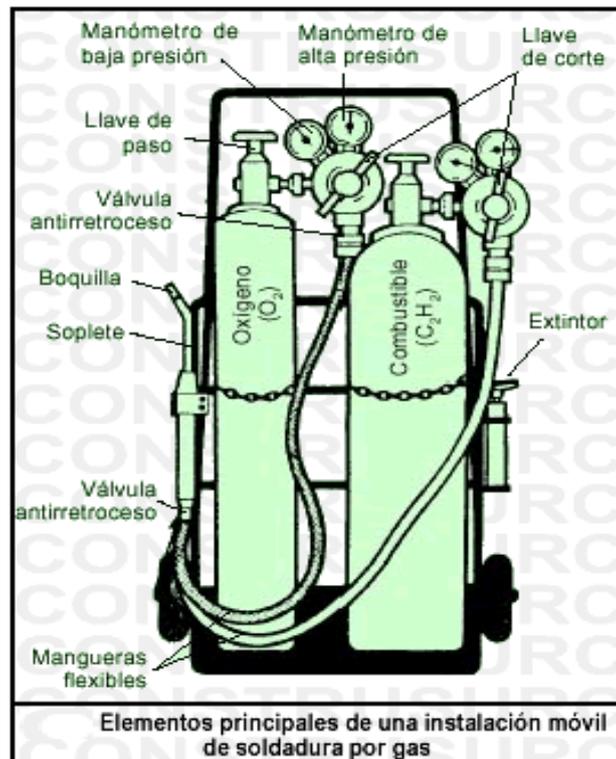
Elementos principales – Soldadura a gas
